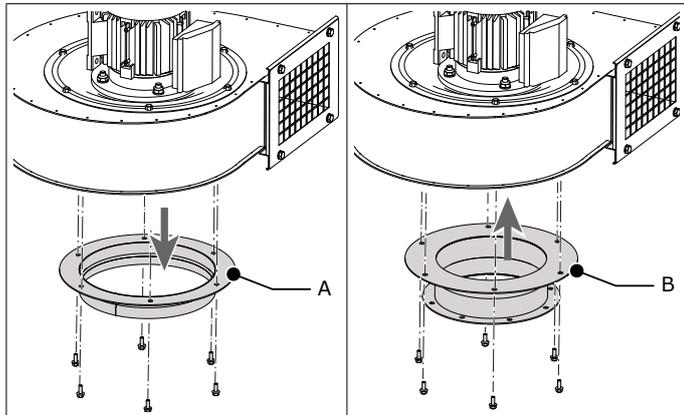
Montaje del adaptador de brazo-ventilador
